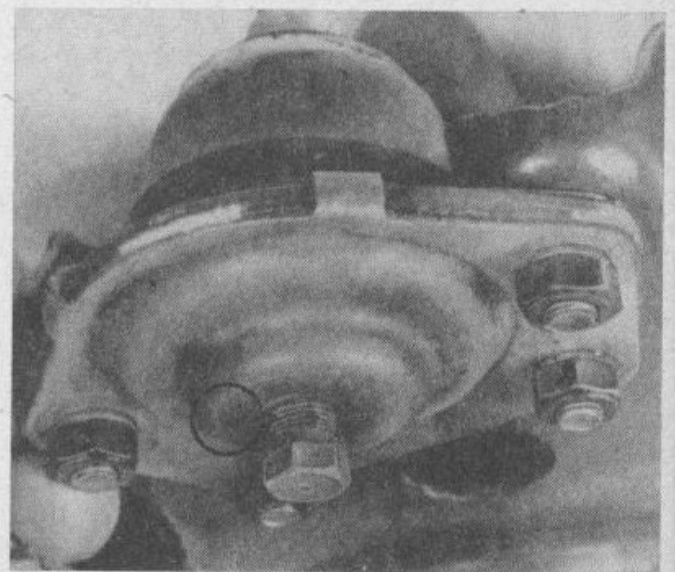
Kugelgelenk des unteren Querlenkers; an Stelle des Gewindestopfens (Pfeil) wird der Schmiernippel eingesetzt
